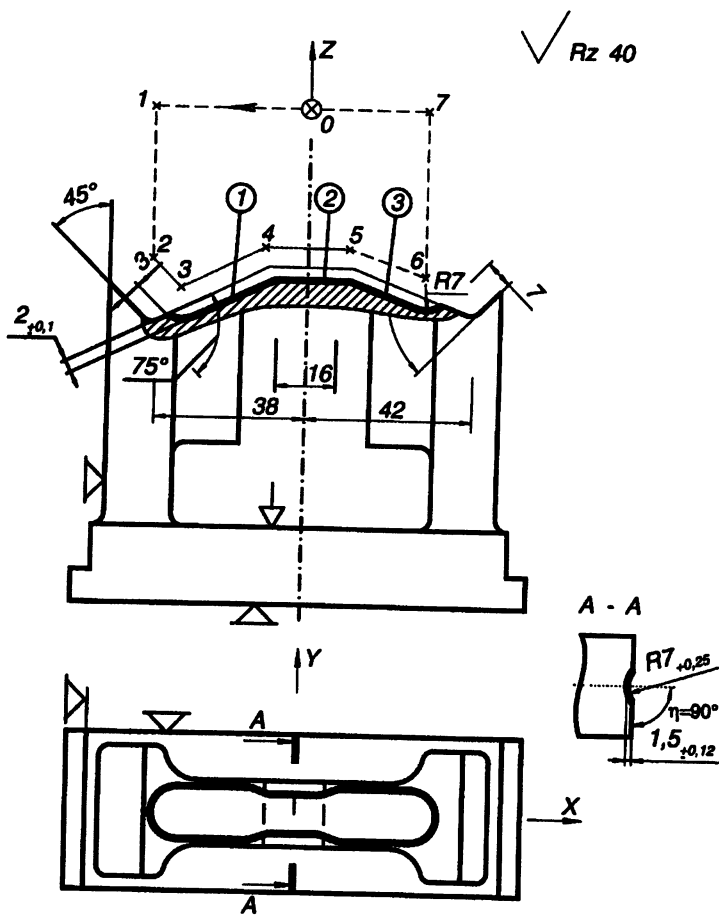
Эскиз детали для примера нормирования операции объемного фрезерования
